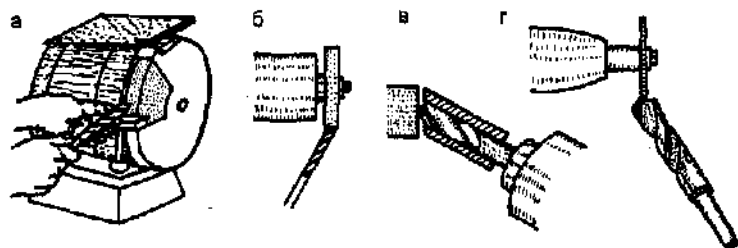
Заточка режущих кромок сверла: а — положение сверла в руках; б — положение сверла относительно шлифовального круга; в — заточка короткого сверла с помощью специальной втулки; г — подточка режущей кромки и передней поверхности
